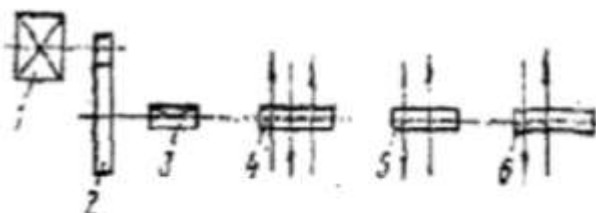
Схема линейного прокатного стана: 1 - двигатель, 2- редуктор; 3 - шестерённая клеть; 4, 5, 6 - рабочие клетки
